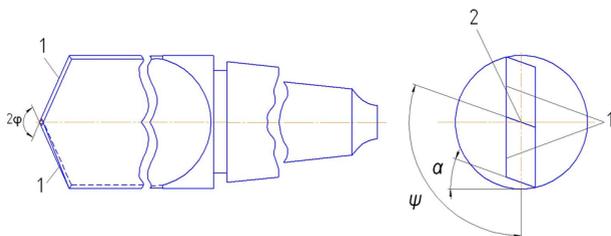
Конструкция перового сверла: 1 – режущие кромки; 2 – сердцевина; 2φ – угол при вершине; ψ – угол наклона поперечной режущей кромки; α – задний угол
